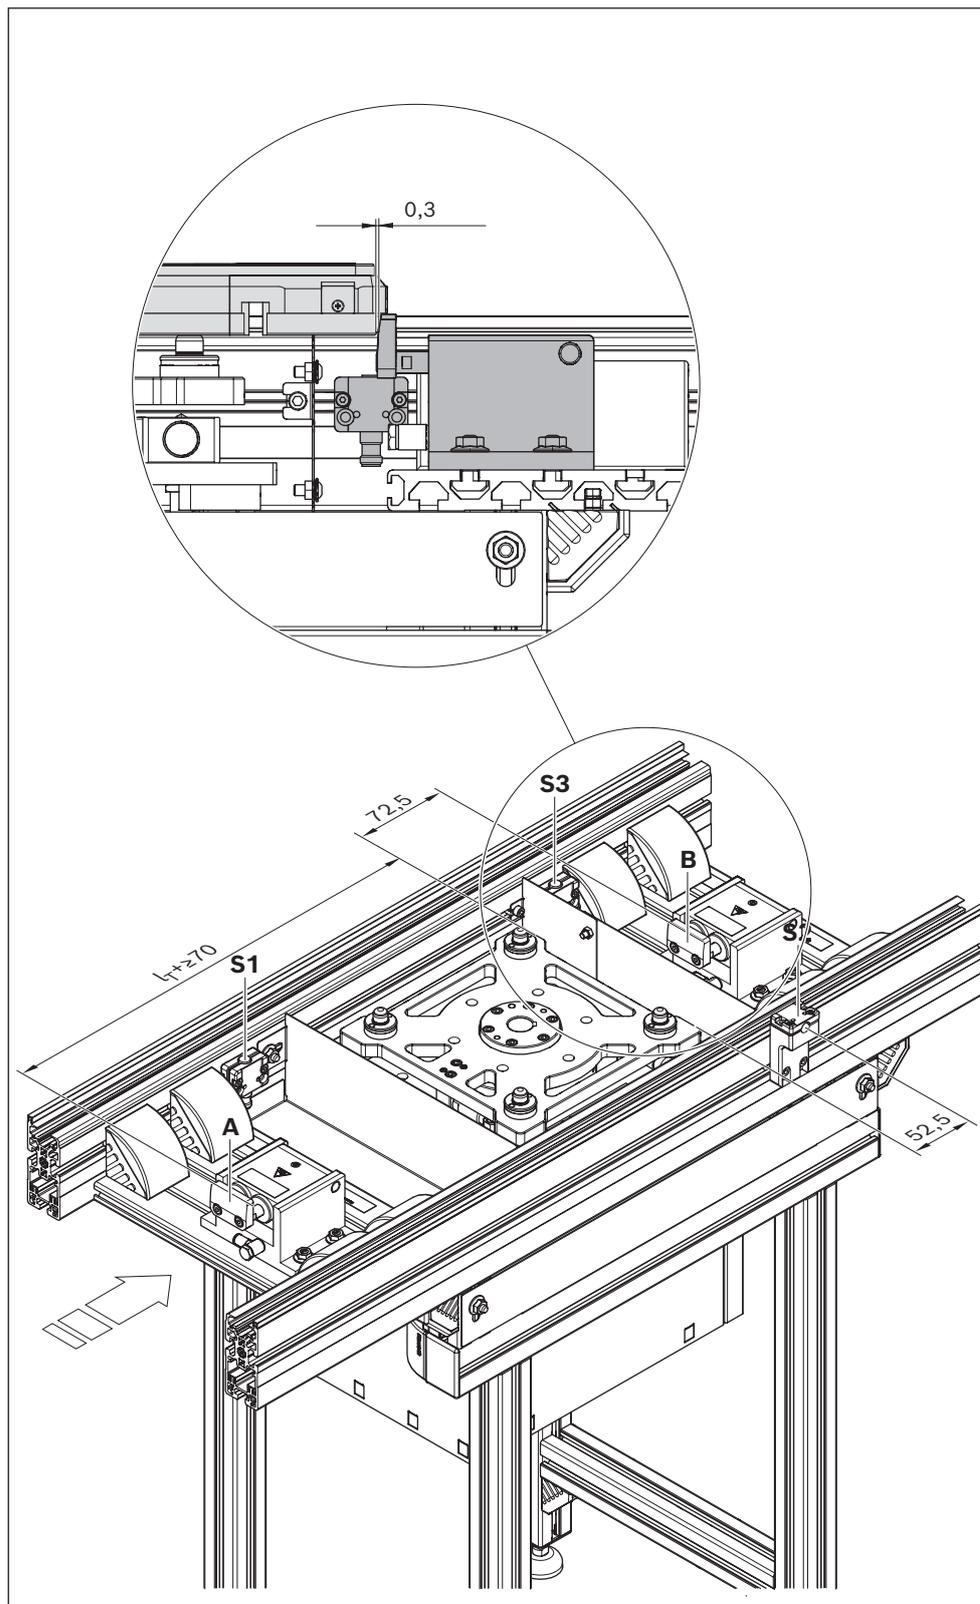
Montaggio di singolarizzatore e interruttore di prossimità
